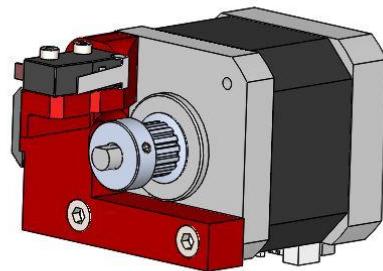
Ensamblaje soporte motor eje y; Fuente: Elaboración propia con SW
